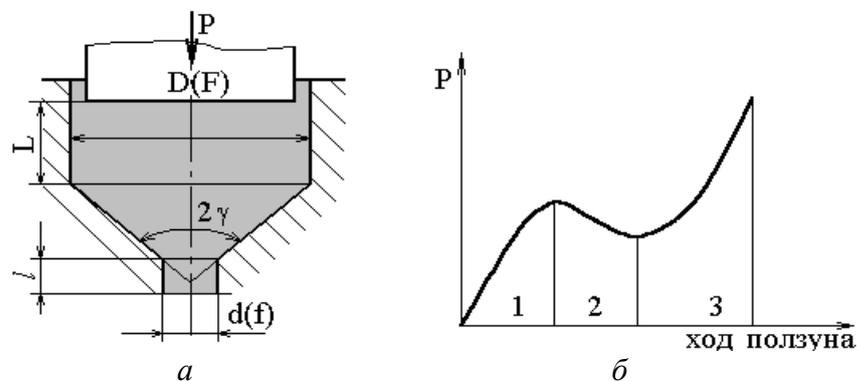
Штамповка выдавливанием: а – схема процесса; б – диаграмма усилия штамповки
